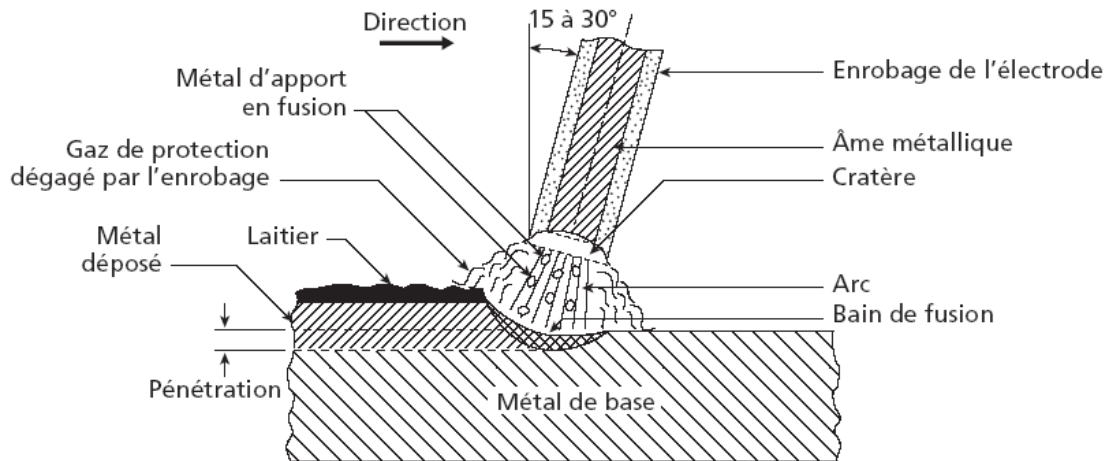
Principe de soudage à l'arc avec électrode enrobée (SMAW)
